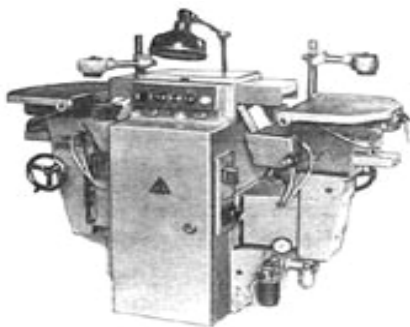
Станок сверлильно-пазовальный СвПГ-2А
